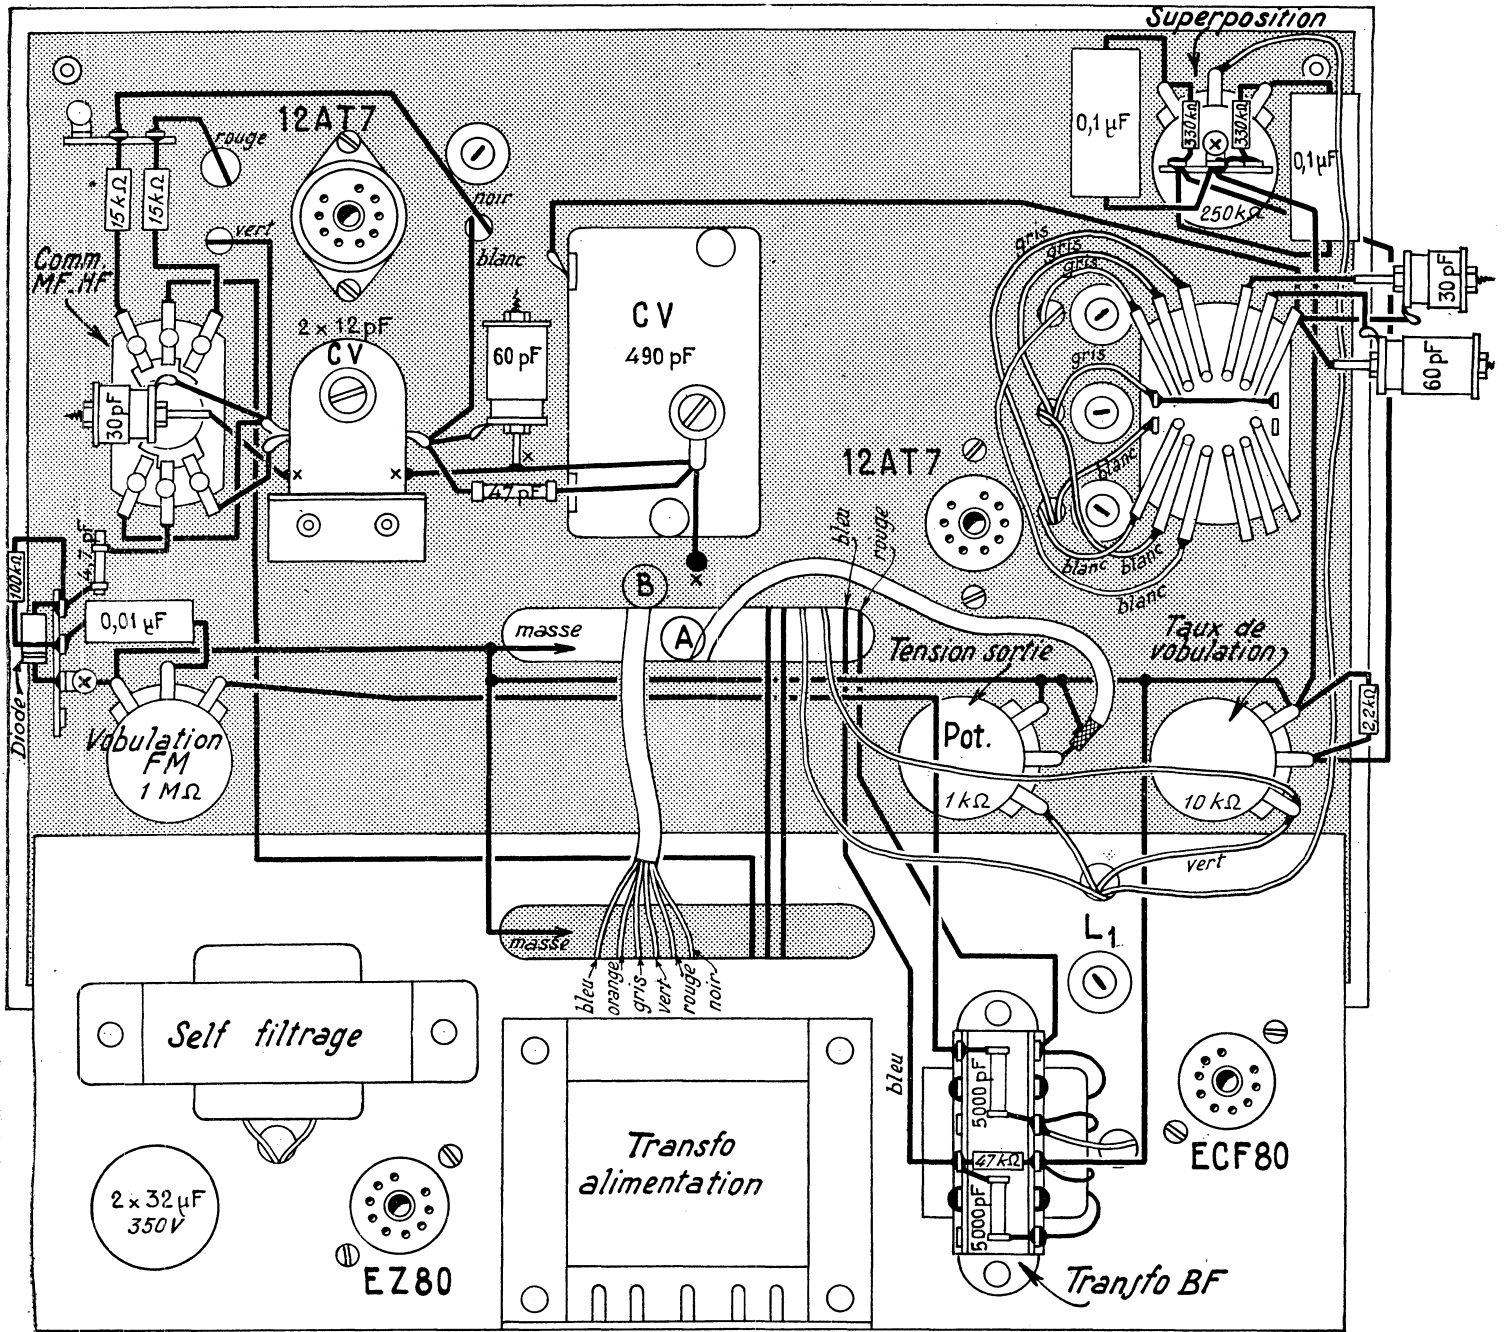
Montage des éléments et câblage sur le dessus du châssis horizontal et sur la face arrière du châssis vertical
